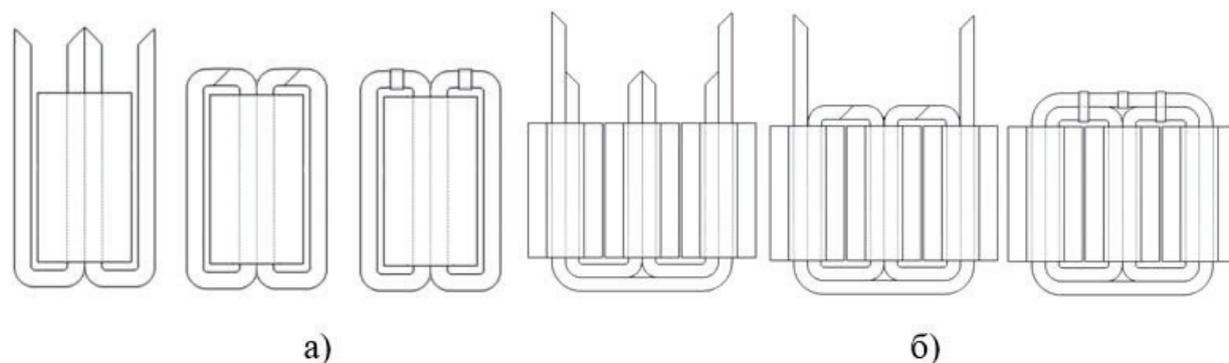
Схема навивки магнитной системы и установки обмоток: а — однофазный трансформатор бронестержневой конструкции; б — трехфазный трансформатор стержневой конструкции
